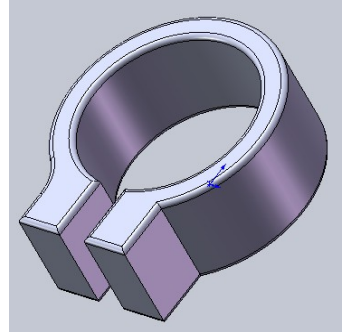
Кінцевий вигляд деталі з округленими поверхнями
